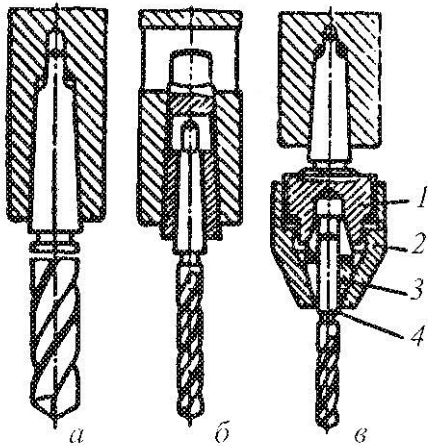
Схеми закріплення інструментів у шпинделі свердильного верстата
